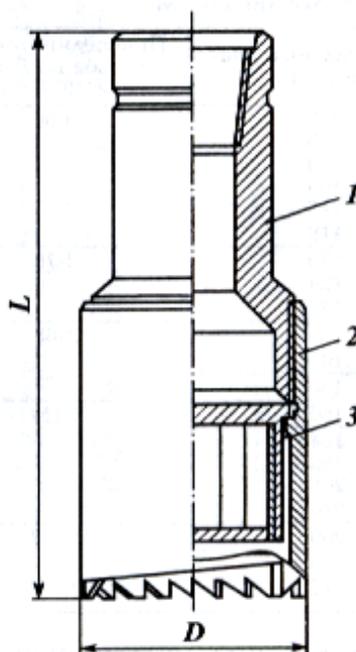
Магнитный фрез-ловитель типа ФМ:
